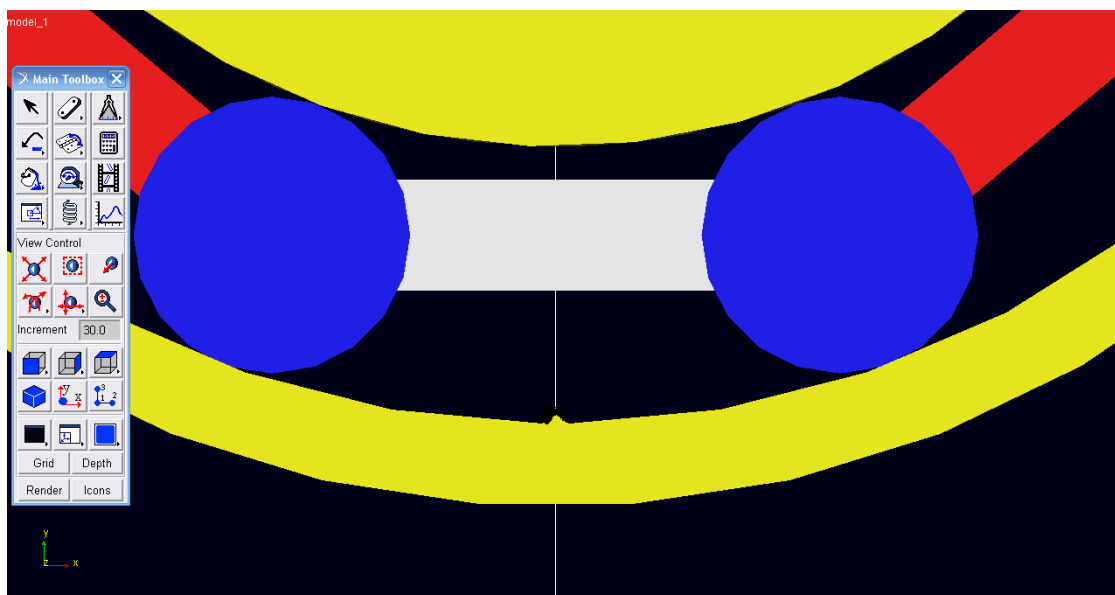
Vista de detalle del alzado del rodamiento con bulto circular en pista exterior de 0,1 mm de radio
